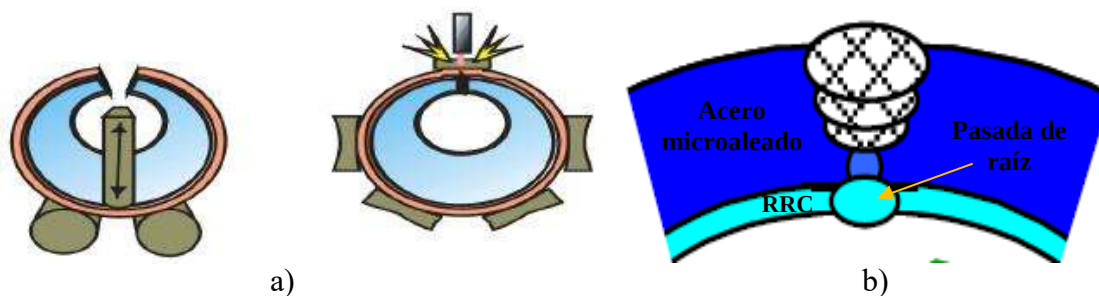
a) Doblado-soldadura y b) cordones de soldadura [5,6].
